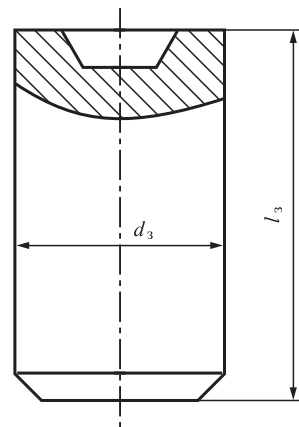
Заготовка, калиброванная осадкой в закрытой матрице
